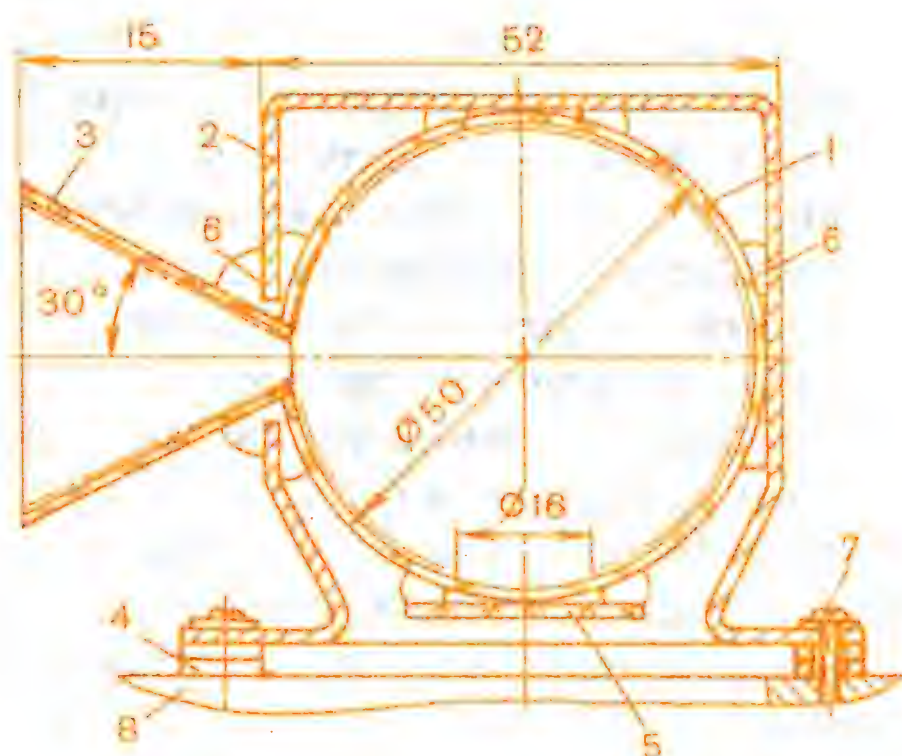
Шар-смеситель: 1 — полый зеркальный шар, 2 — конус, 3 — хомут крепежный, 4 — клей эпоксидный, 5 — матовое стекло, 6 — винт, 7 — шайбы, 8 — цветоголовка
